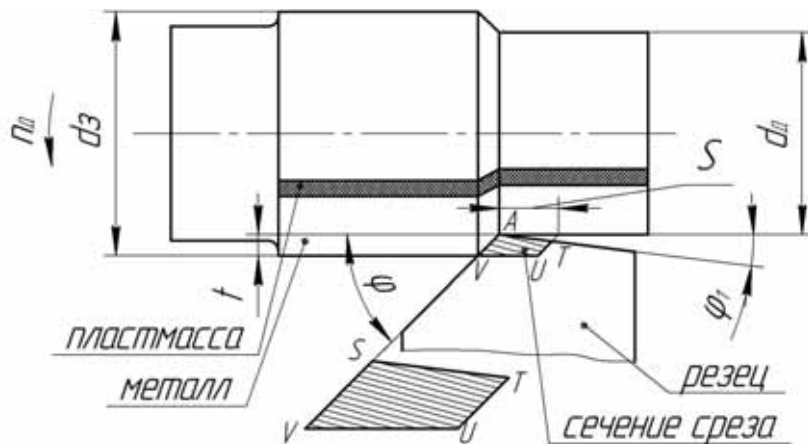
Возможные варианты контакта реза с обрабатываемой поверхностью
